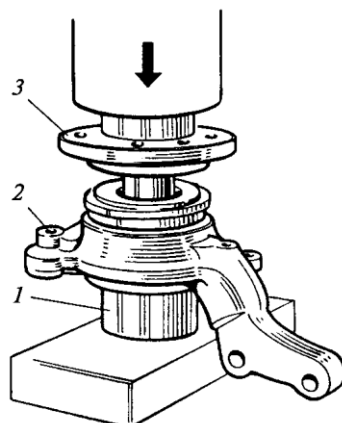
Запрессовка ступицы колеса на настольном пневматическом прессе: 1 — оправка; 2 — поворотный кулак; 3 — ступица
